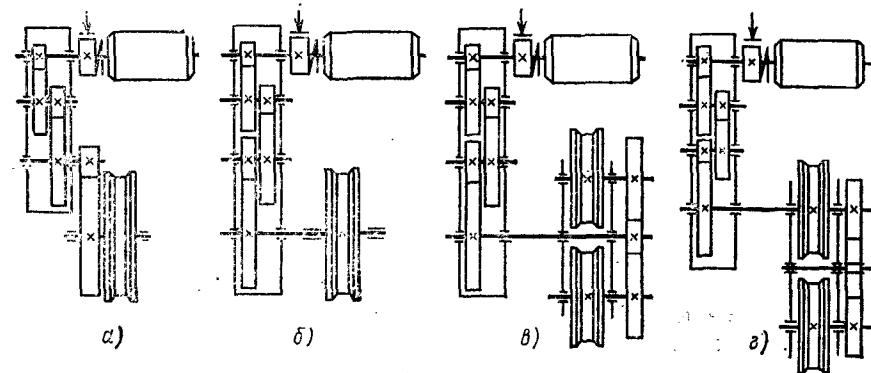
Схемы механизмов передвижения козловых кранов: а) — с двухступенчатым редуктором; б) — с трехступенчатым редуктором; в, г) — с балансиром
